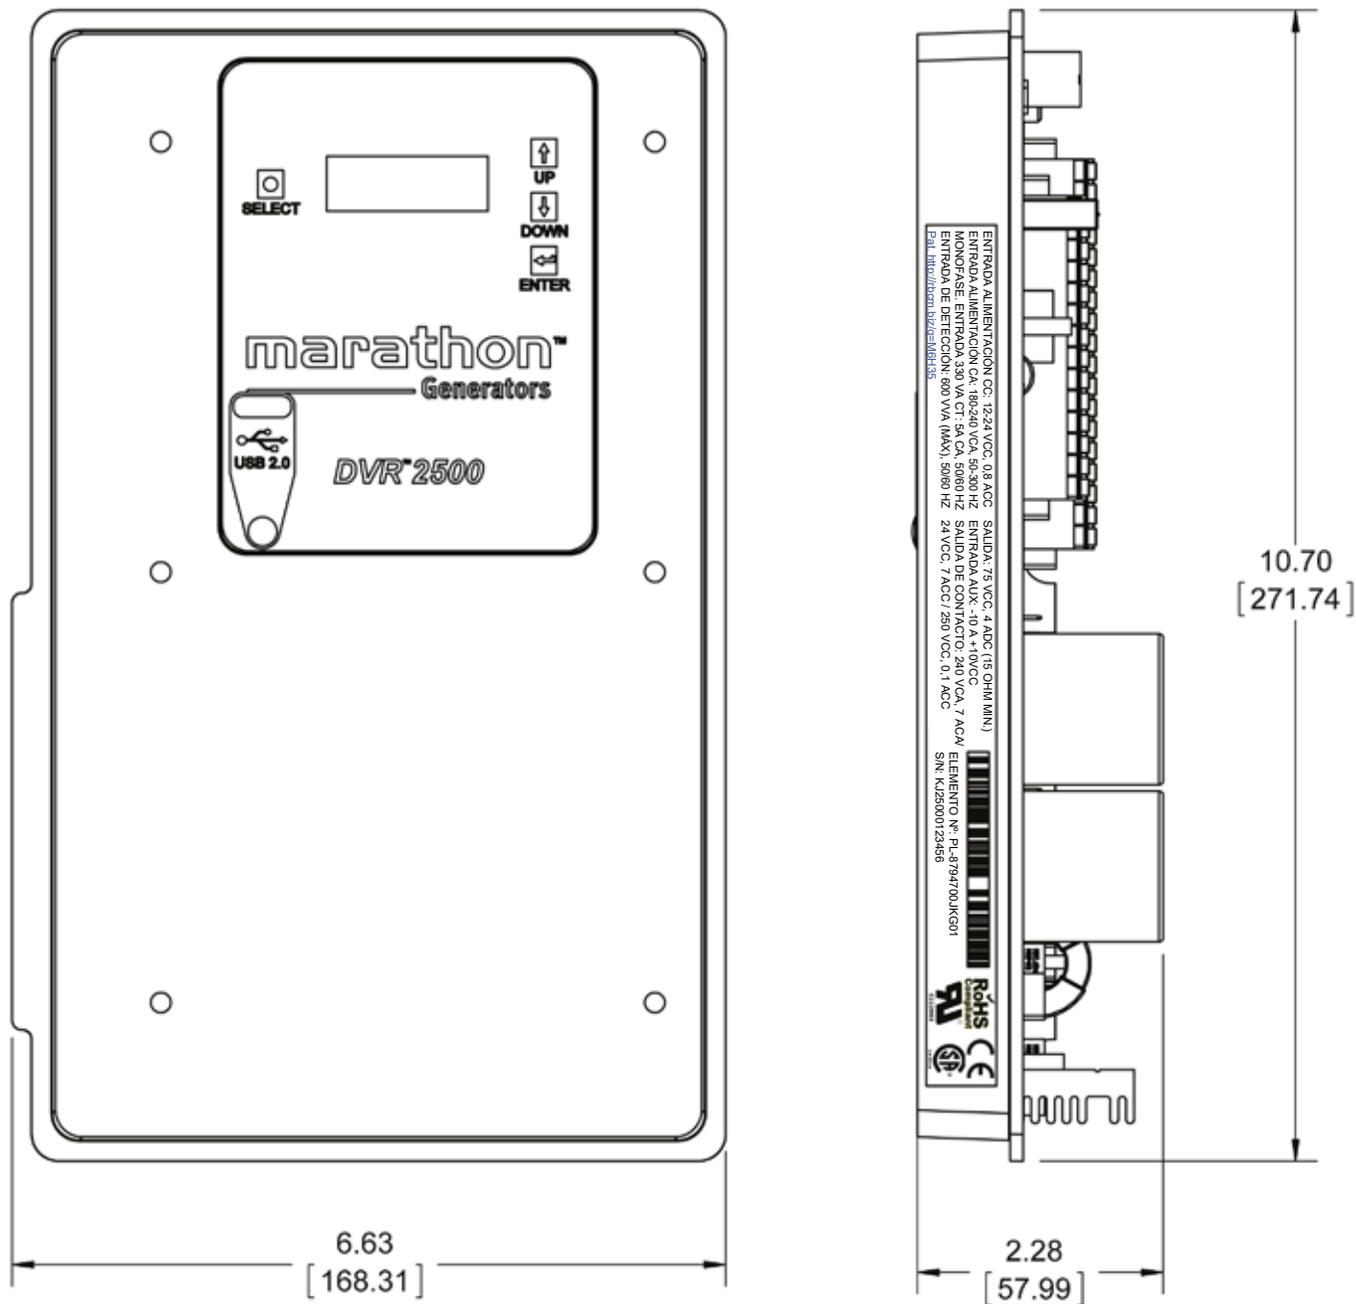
Dimensiones del frente del 2500 sin tapa. Válido para versiones 2400 y 2500.
